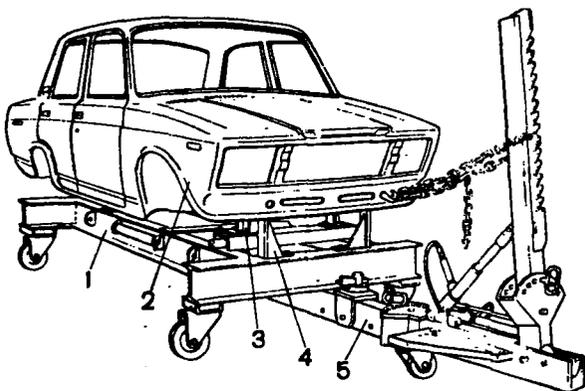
Установка для контроля и ремонта кузовов с приспособлением для правки: 1 - рама установки; 2 - кузов автомобиля; 3 - кронштейн крепления поперечины передней подвески; 4 - кронштейн крепления стабилизатора поперечной устойчивости; 5 - приспособление для правки со стрелой и гидравлическим устройством
